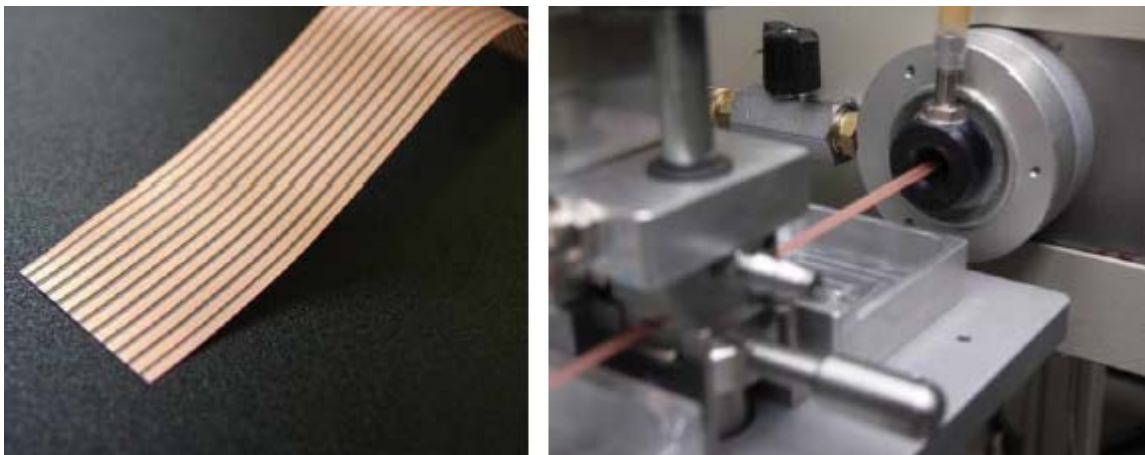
и 17 Гибкий плоский кабель и головка-аппликатор для нанесения полимера
